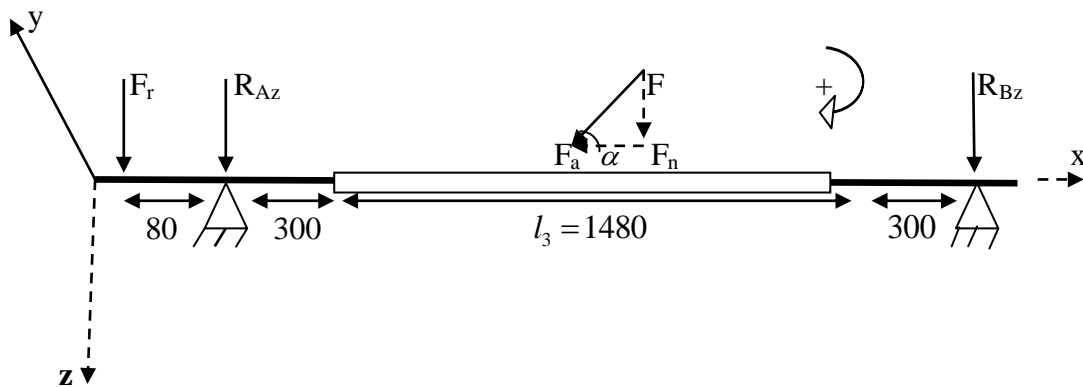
Schéma illustre les efforts sur la barre dans le plan (xoz).
